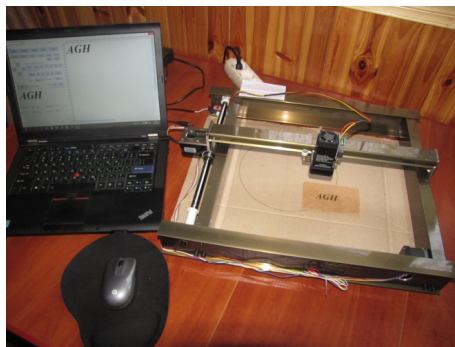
Загальний вигляд пристрою для лазерного різання
